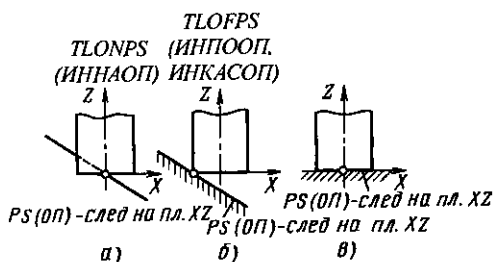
Положения инструмента относительно обрабатываемой поверхности PS (ОП)
